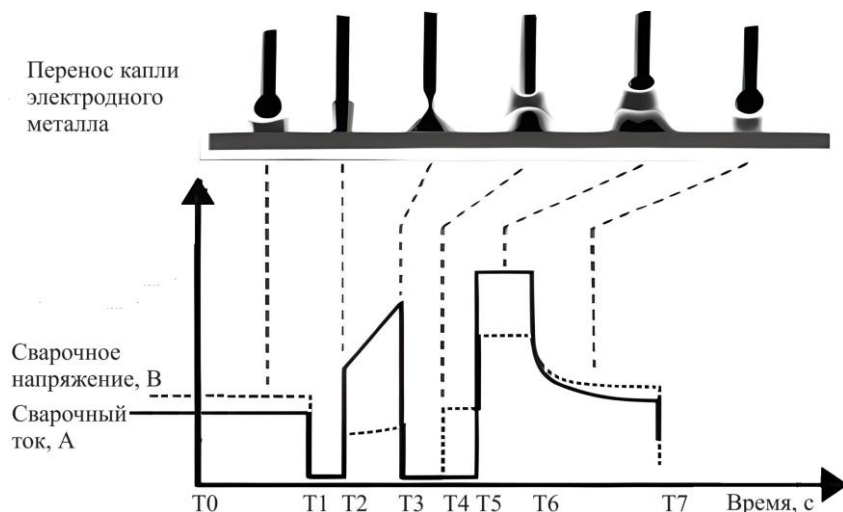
Формы кривых сварочного тока и напряжения при сварке методом *STT
